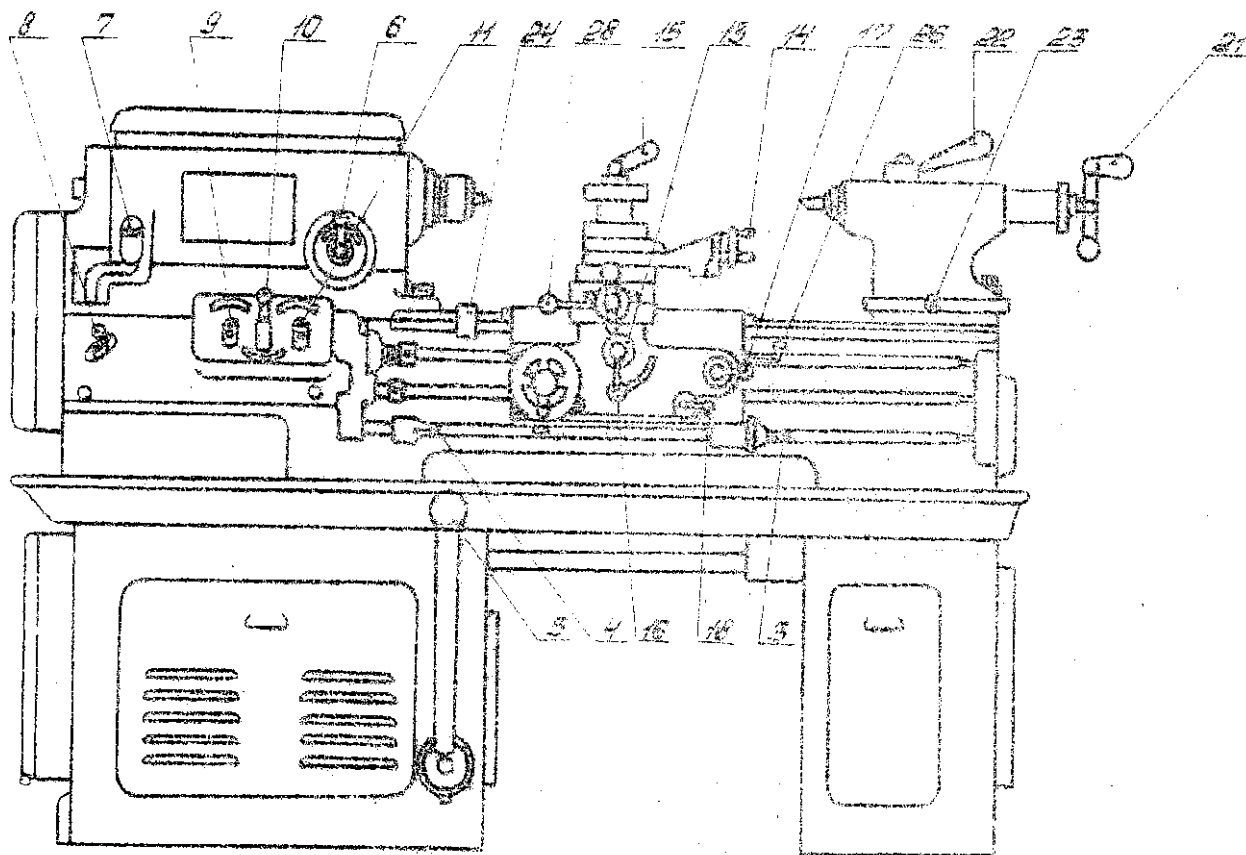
Токарно-винторезный станок ИЕ6ИМТ (органы управления)
